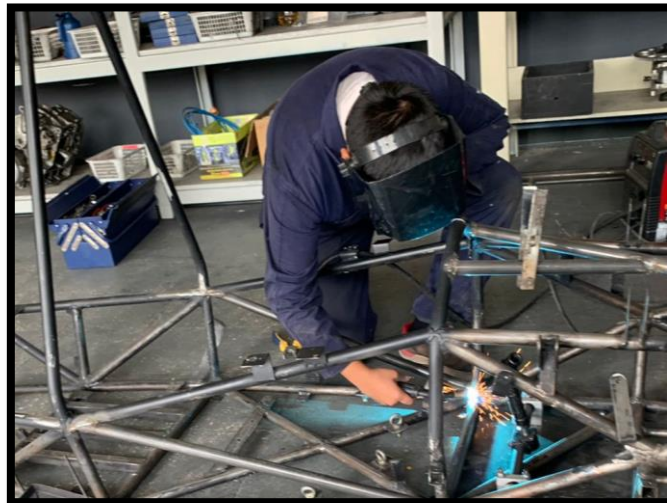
Soldadura de tirantes delanteros entre mampara delantera y frontal
